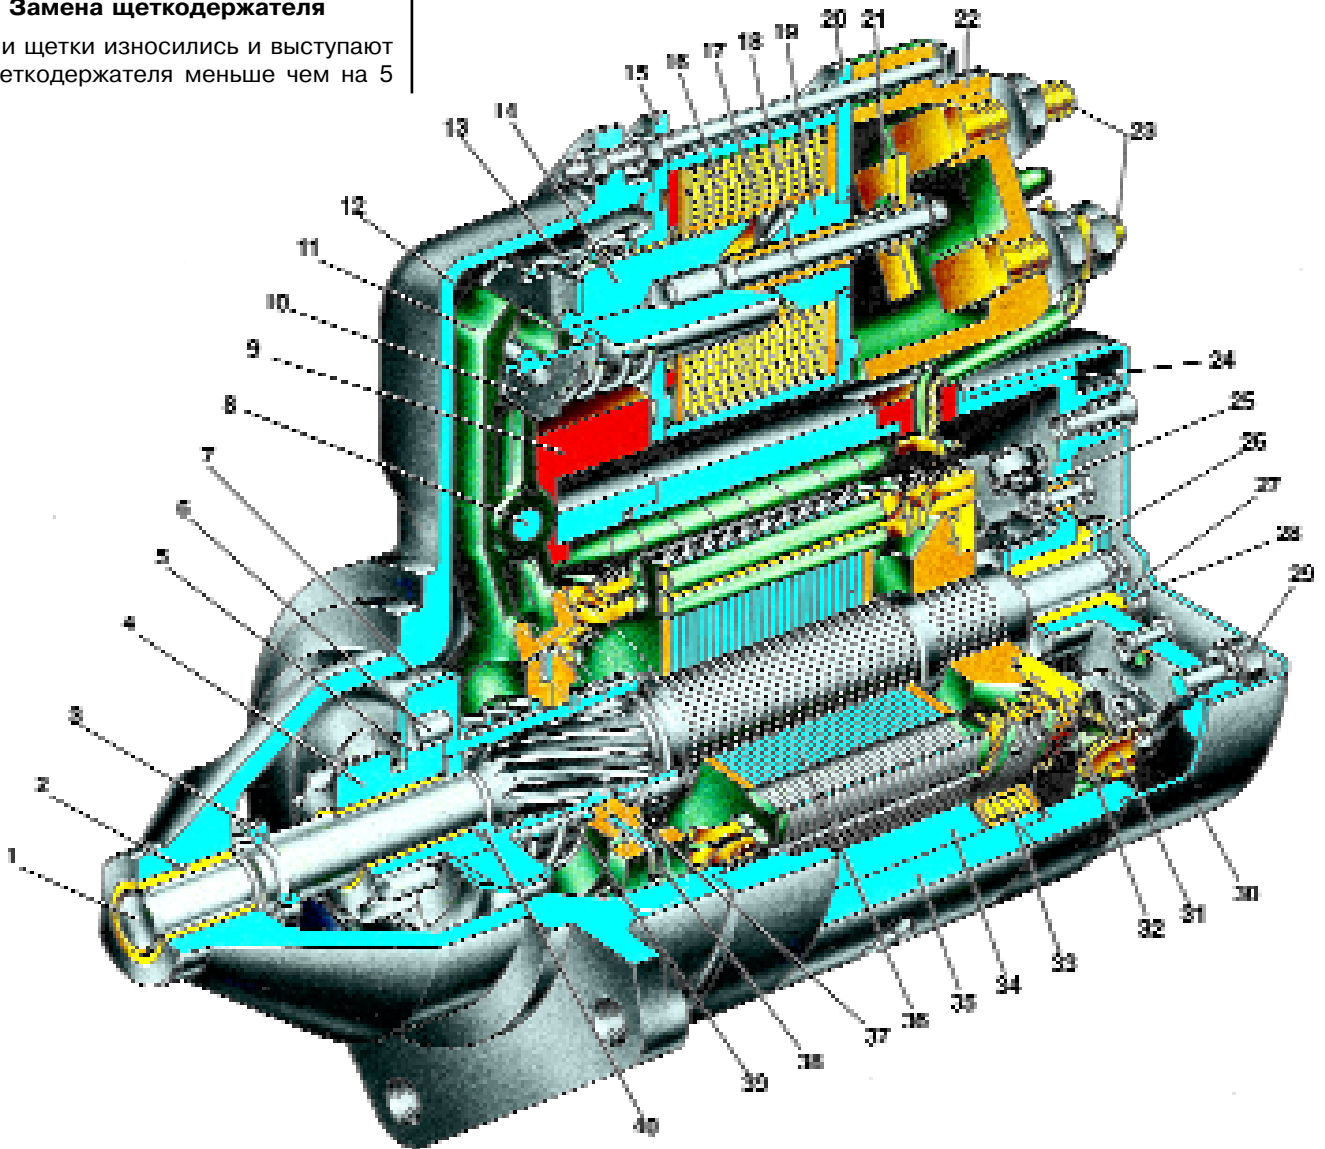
Стартер 35.3708: 1 — вал якоря; 2 — втулка крышки стартера; 3 — ограничительное кольцо хода шестерни; 4 — шестерня привода с внутренним кольцом обгонной муфты; 5 — упорное полукольцо; 6 — ролик обгонной муфты; 7 — кожух обгонной муфты; 8 — ось рычага привода; 9 — заглушка; 10 — тяга якоря реле; 11 — рычаг привода; 12 — крышка со стороны привода; 13 — возвратная пружина якоря реле; 14 — якорь реле стартера; 15 — передний фланец реле; 16 — удерживающая обмотка реле; 17 — втягивающая обмотка реле; 18 — шток якоря; 19 — сердечник реле; 20 — фланец сердечника; 21 — кон-
